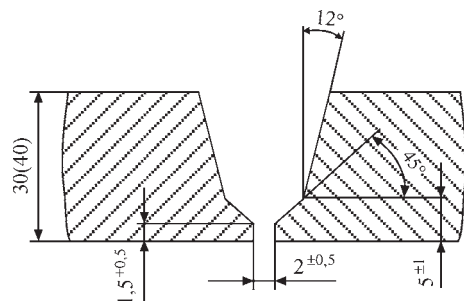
Форма обробки кромки з'єднання сталі СА-6NM для механізованого зварювання
